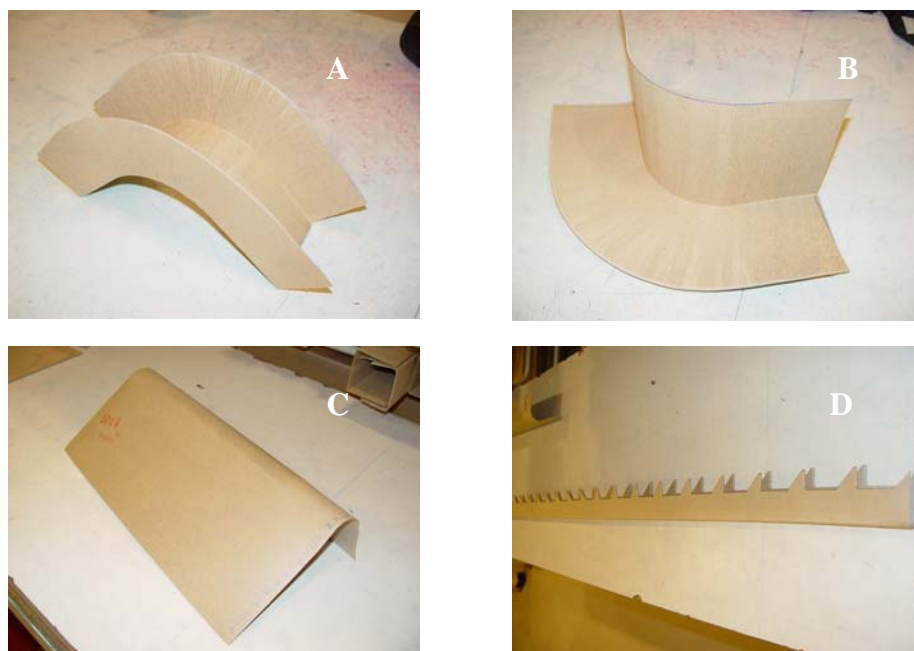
(A) - Moldado Curvo Interior em U, (B) – Moldado Curvo Interior em L, (C) Moldado Recto em L e (D) Moldado Recto em U com entalhes
